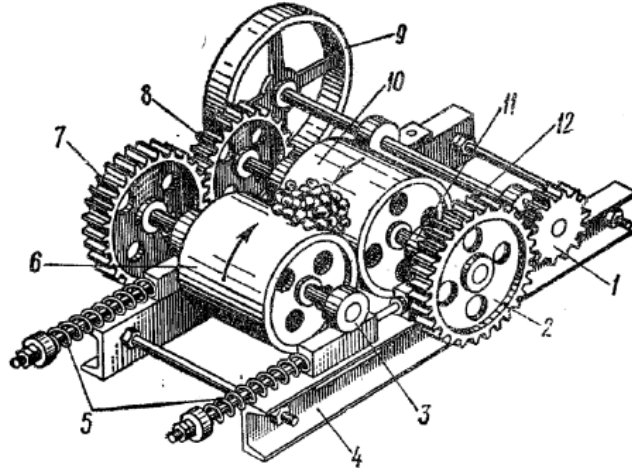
Схема валкової дробарки з гладкими валками й шестеренчастим приводом
